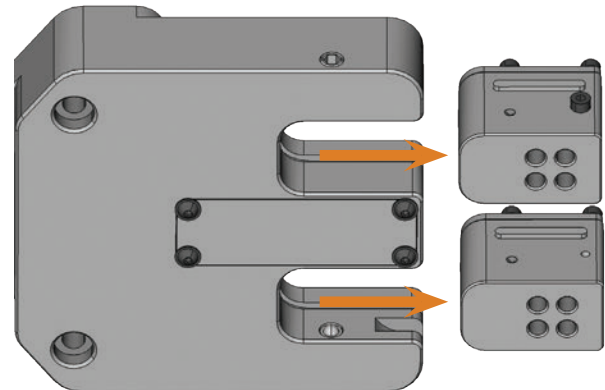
HERAUSZIEHEN DER WERKZEUGMAGAZINE
